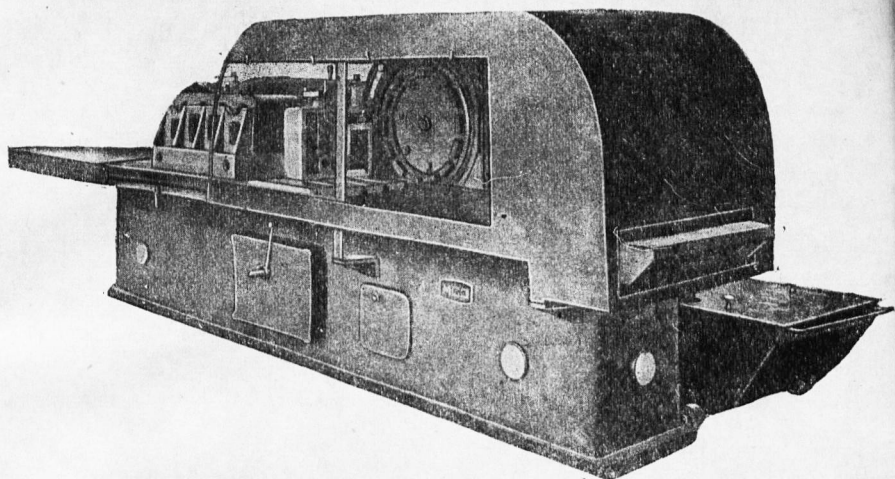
Общий вид плоскошлифовального станка 373-С Московского завода шлифовальных станков
